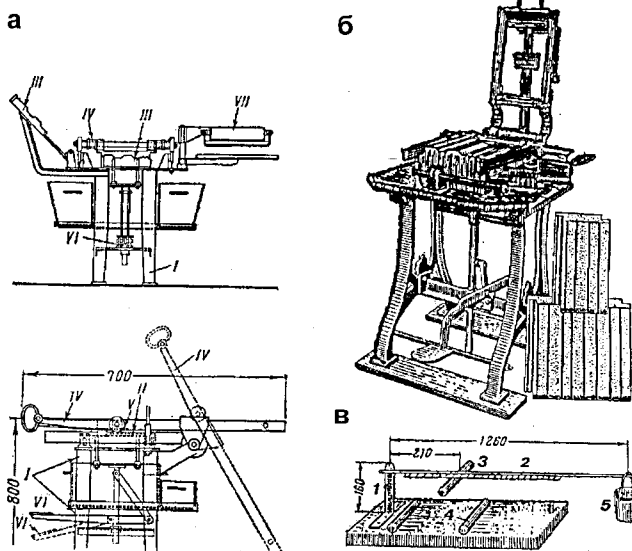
Устаткування для виробництва цементно-піщаної черепиці: а - верстат з кареткою; б - верстат з ручним гладилом; в - схема важливого пристрою для випробування черепиці на злам: 1 - вертикальний стоек; 2 - металевий стержень; 3 - верхній опорний каток; 4 - нижні катки; 5 - вантаж.
